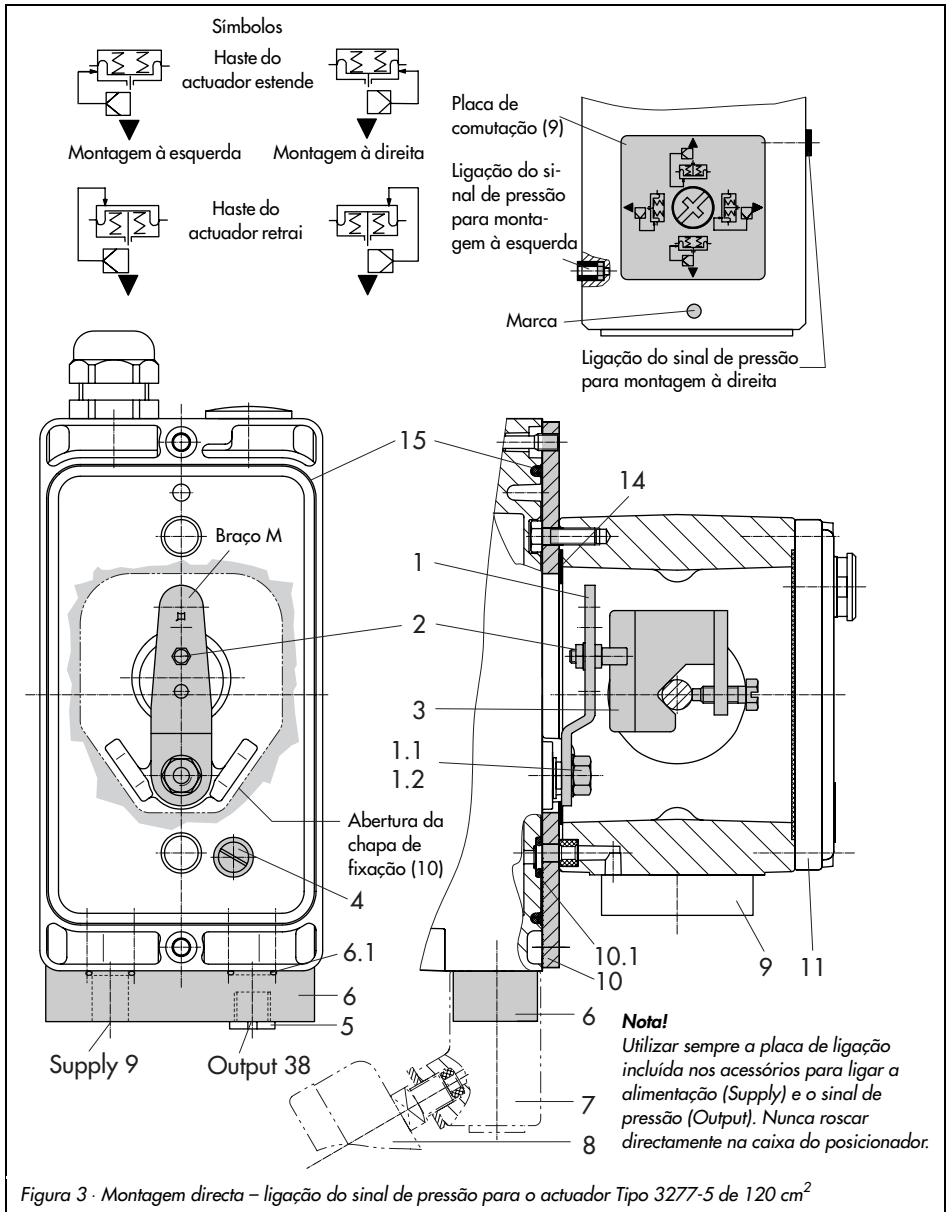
Montagem directa - ligação do sinal de pressão para o actuador Tipo 3277-5 de 120 cm<sup>2</sup>
